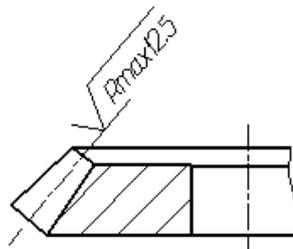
Пример обозначения различной шероховатости на одной поверхности
